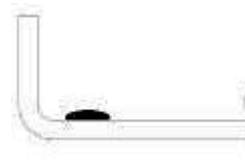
Ensamblaje del conjunto panel exterior panel exterior
